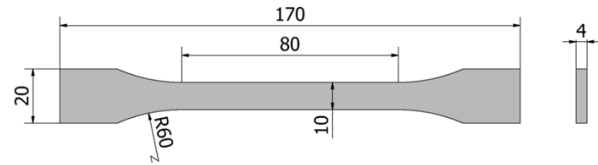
Geometría de las probetas de tracción. Dimensiones en mm.
